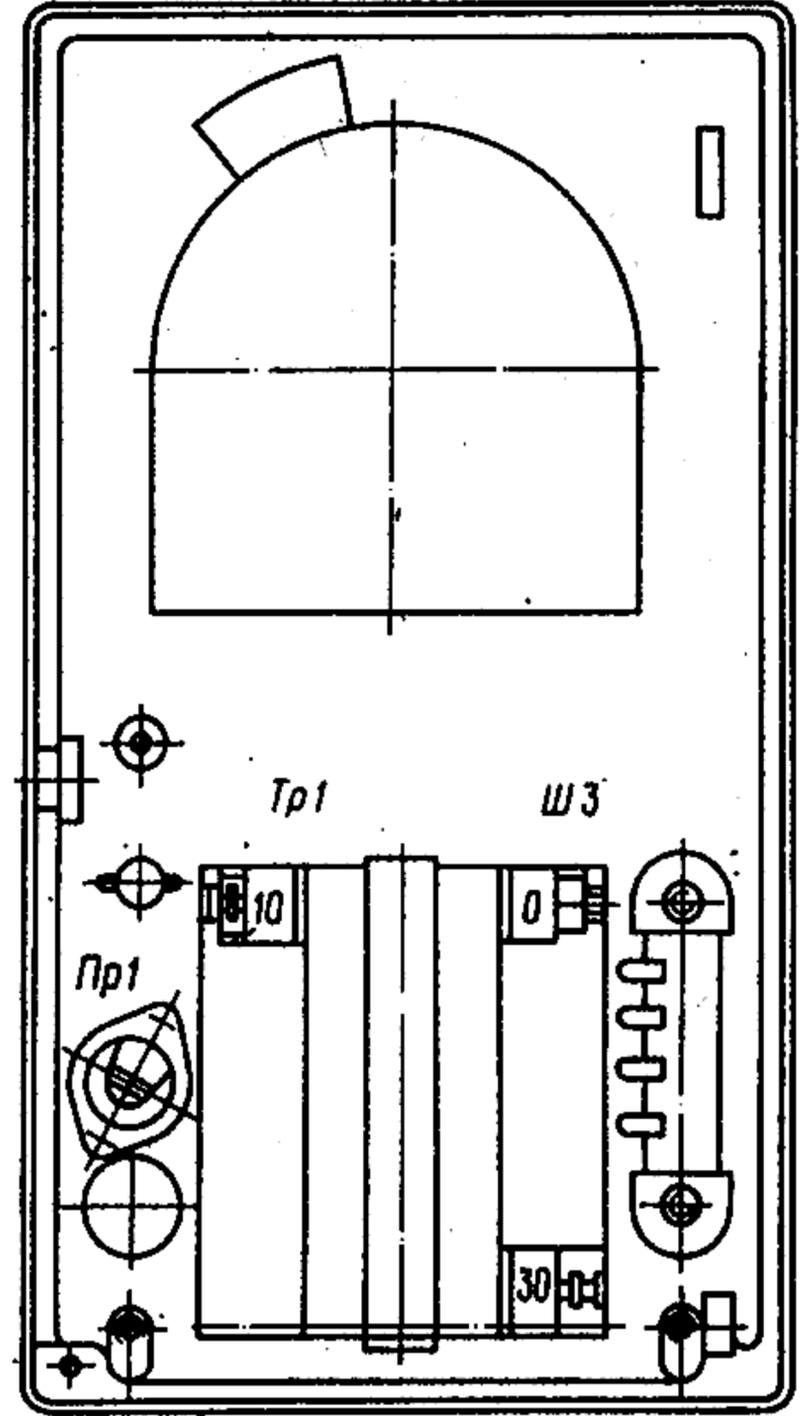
Plan de disposition des éléments sur le panneau arrière
